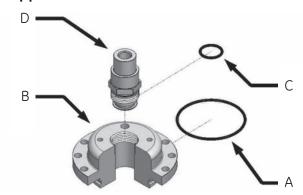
Assemblaggio collo tenuta 1000/1500-CH
